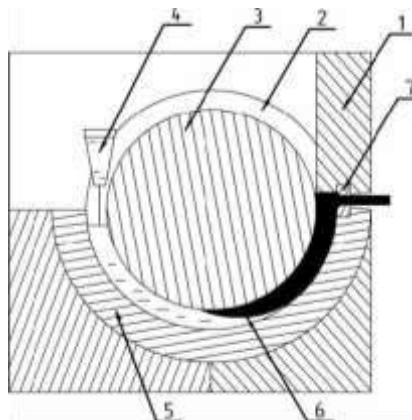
Схема установки для непрерывного литья и прессования Кастэкс:
